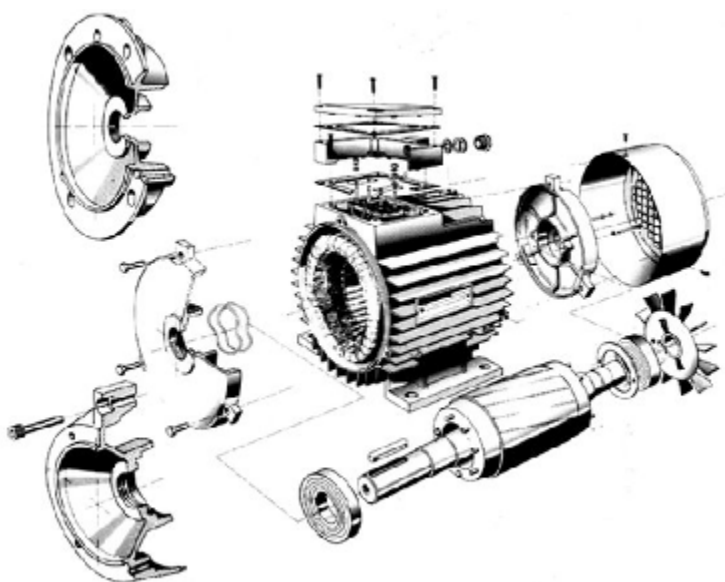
"Projeção" do motor assíncrono de rotor em gaiola de esquilo.
